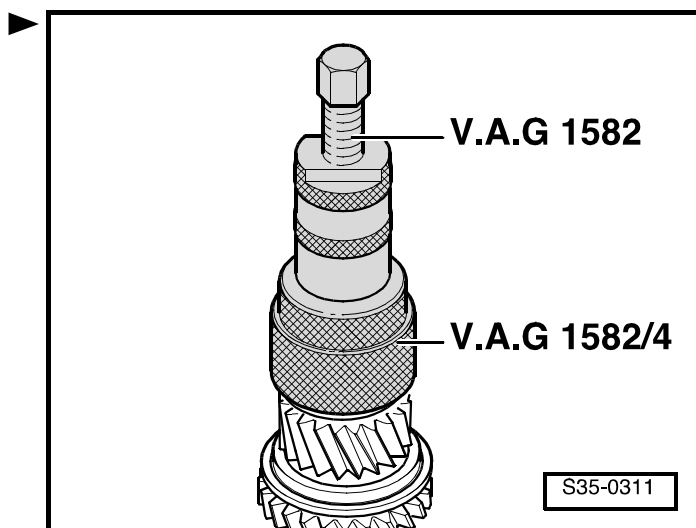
Положение для сборки каретки синхронизатора для передачи заднего хода
